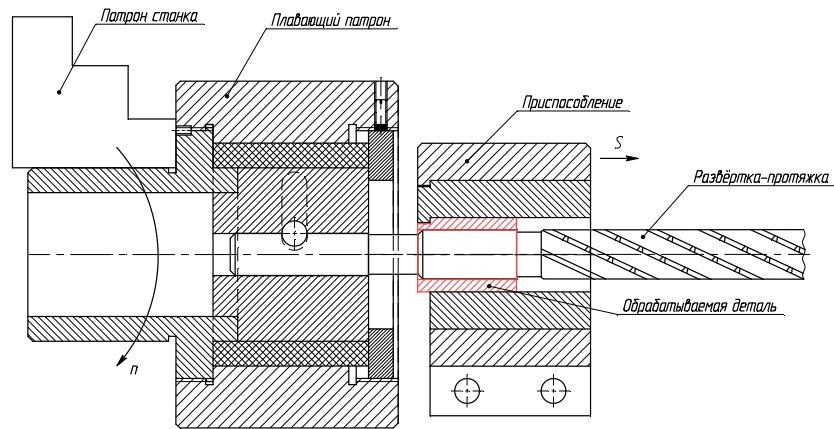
Схема обработки отверстий развёрткой-протяжкой с применением плавающего патрона
